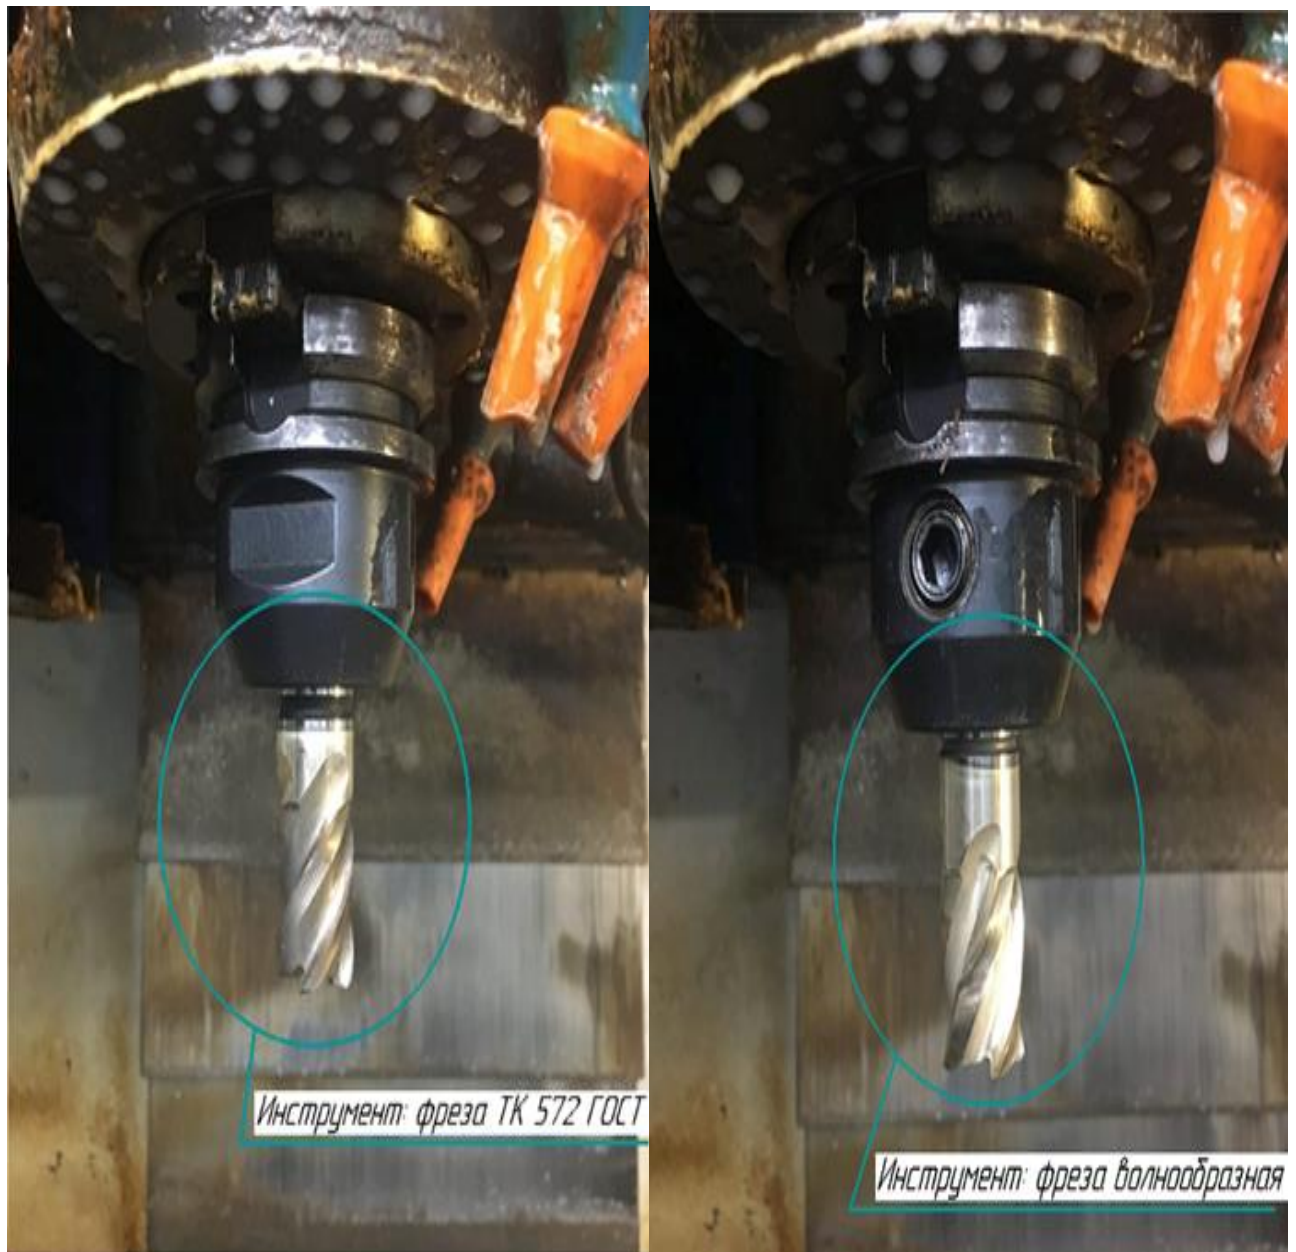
Схемы крепления фрез концевых, ГОСТ, и «волнообразных»
